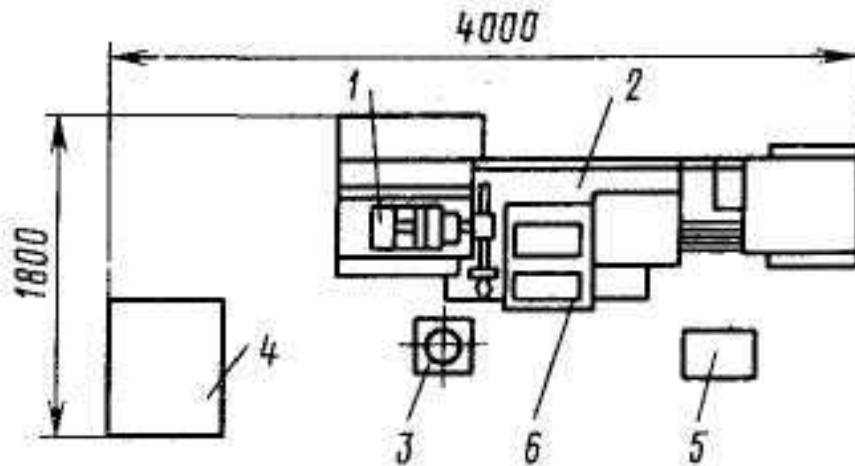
Компоновка верстатного комплексу на базі токарно-гвинторізного верстата 1И611ПМФ3 із ЧПК
